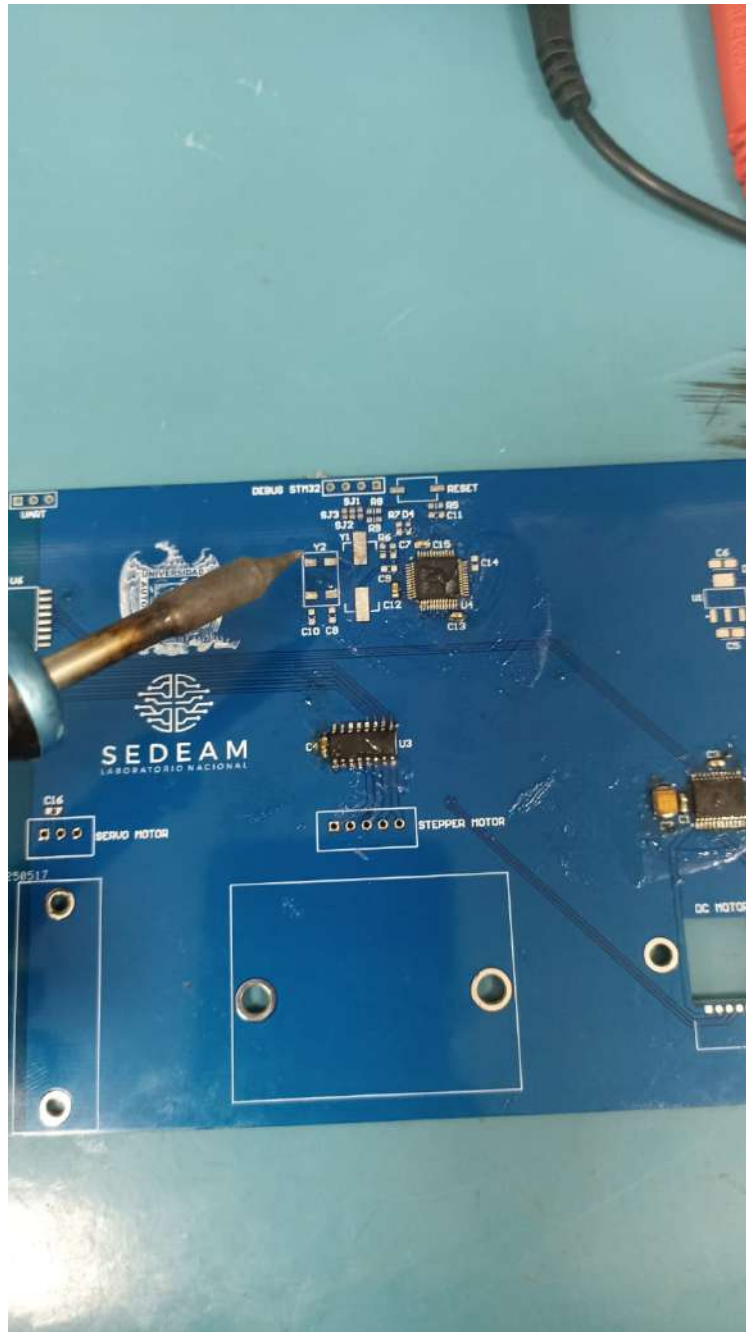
Proceso de soldadura de componentes SMD en la tarjeta final.
